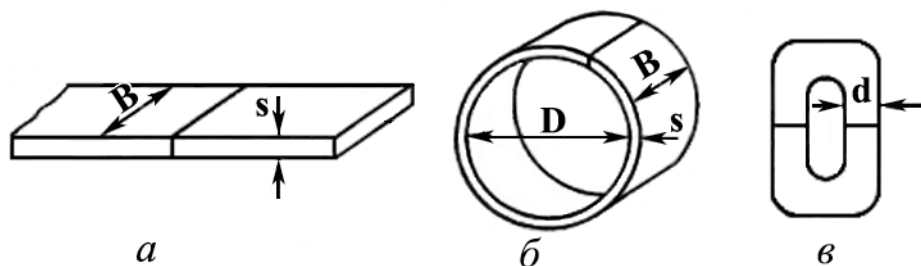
Примеры типовых соединений, получаемых стыковой сваркой
